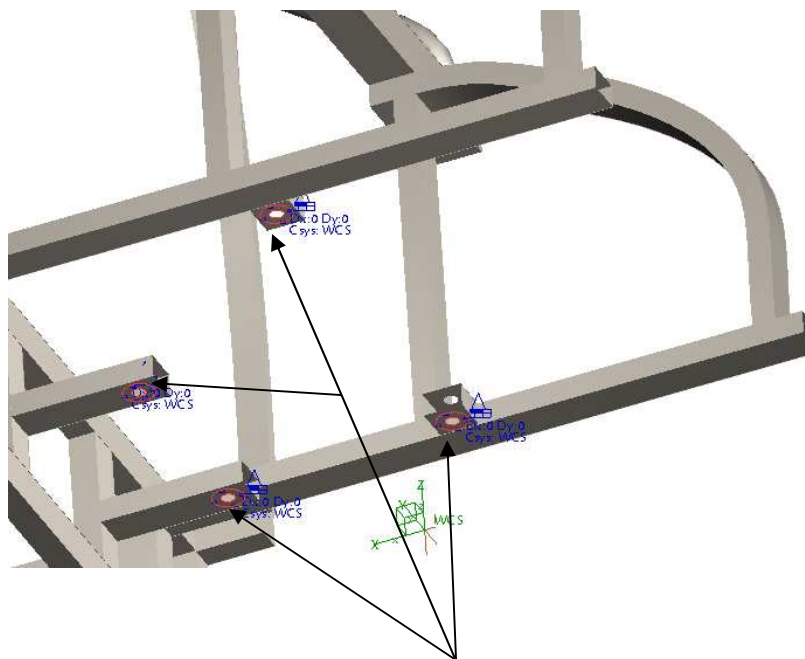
Surface region a zamezení posuvu u uložení pružiny zadní nápravy
